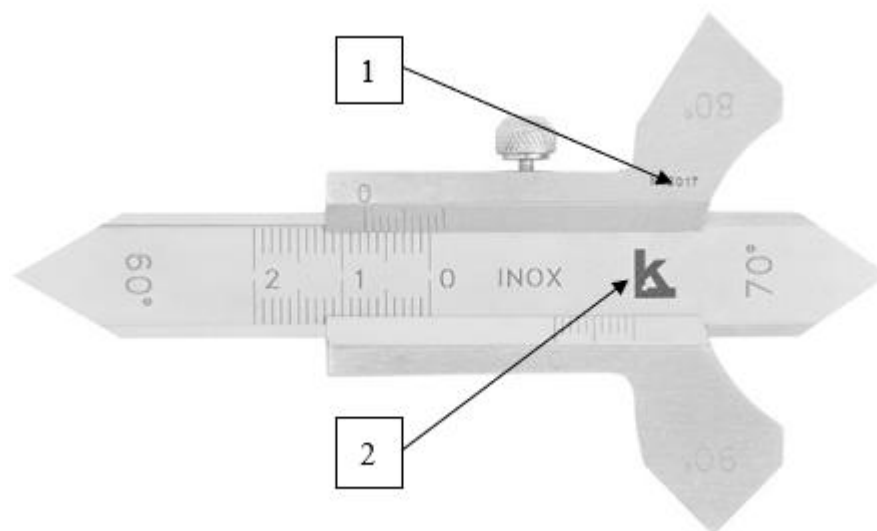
Общий вид шаблона сварщика Ушера – Маршака
